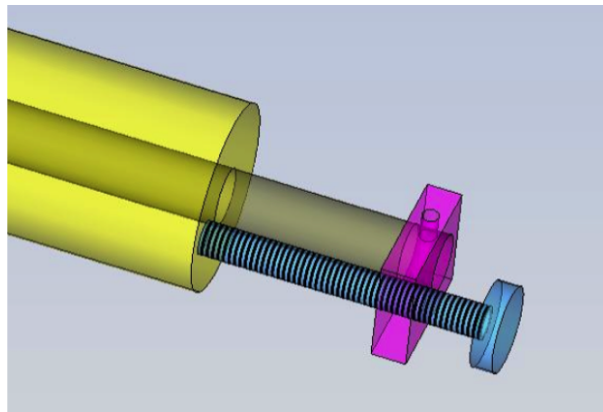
Struttura di immissione del campione: una vite (in azzurro) permette di immettere ed estrarre il portacampione fissato all'estremità della barra metallica posta a fianco della vite e collegata ad essa tramite un supporto (in viola). Sulla sinistra è posto l'ingrassatore (giallo), prima del collegamento con la flangia della camera.
